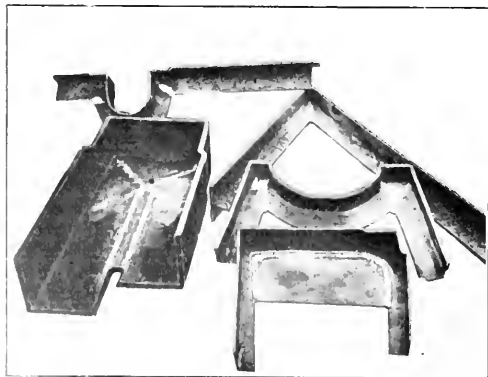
PIEZAS SOLDADAS ELÉCTRICAMENTE
